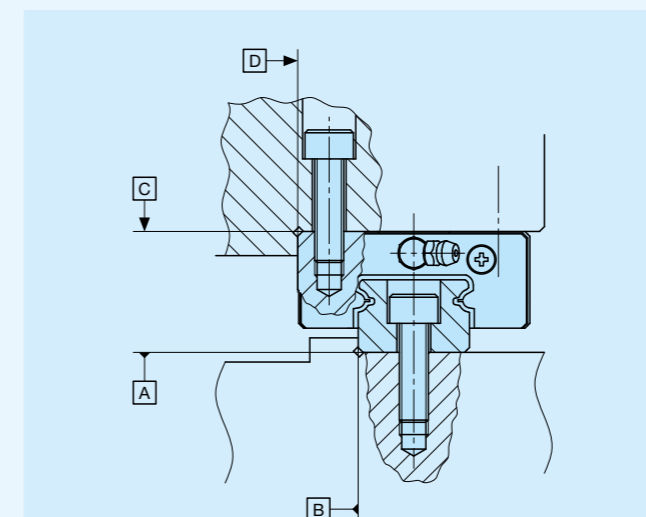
Superfície de montagem de referência e estrutura de montagem típica
